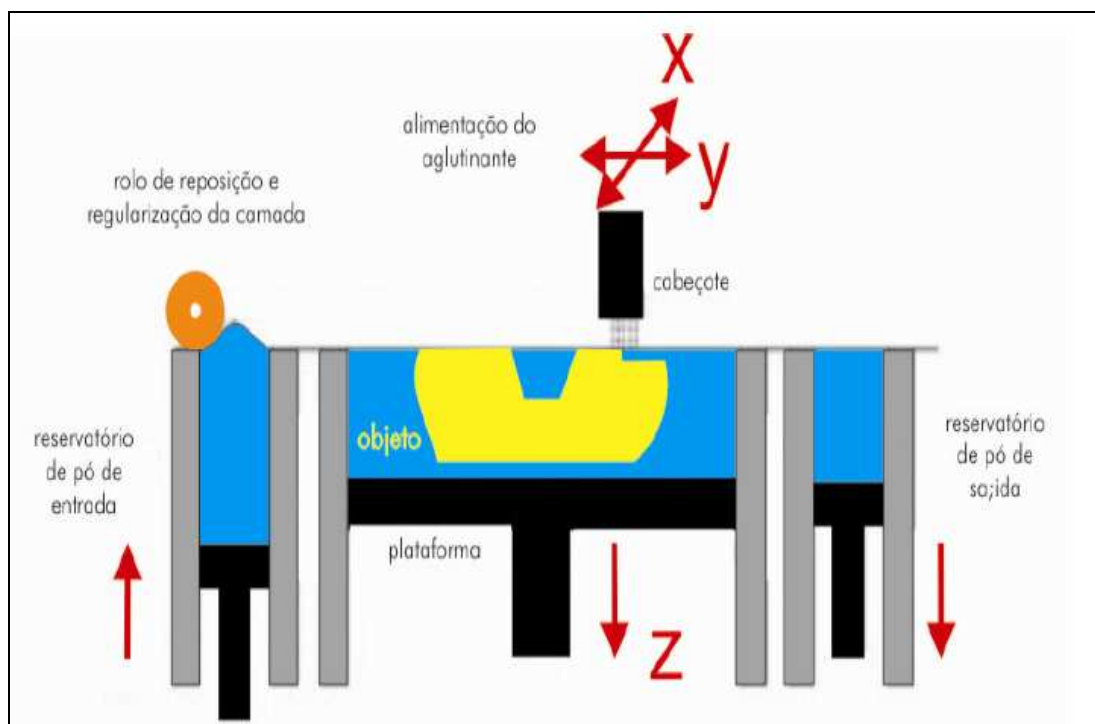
Processo de deposição de lâminas (Milwaukee School of Engineering, 2011).
